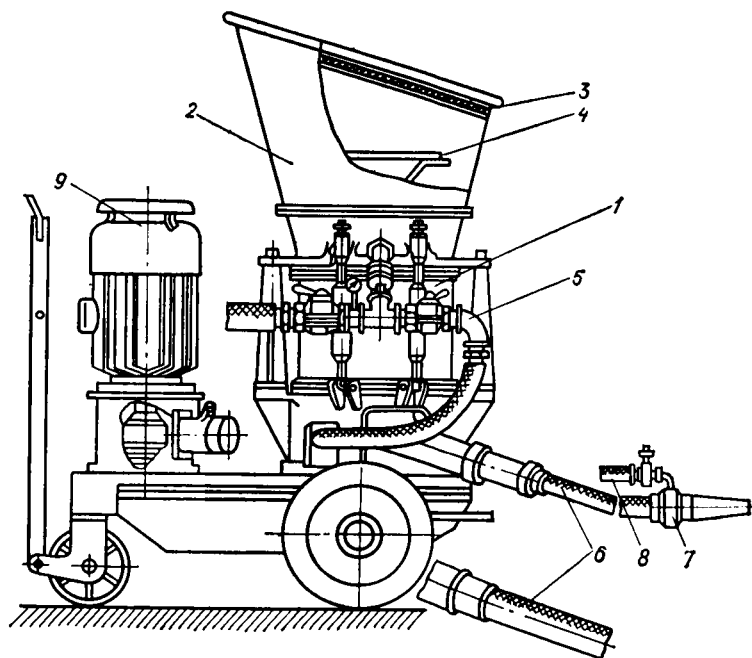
Машина для набрызг-бетонных работ БМ-68У:
